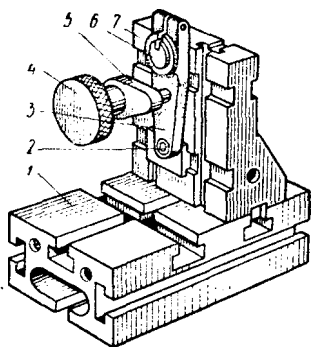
Универсально-сборное приспособление для обработки паза зажима в рычагах
